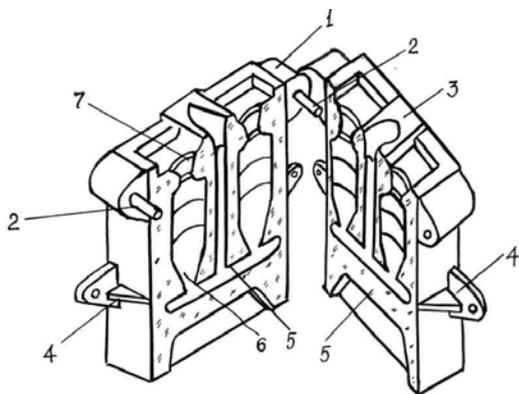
Кокиль для отливки корпуса снаряда.
